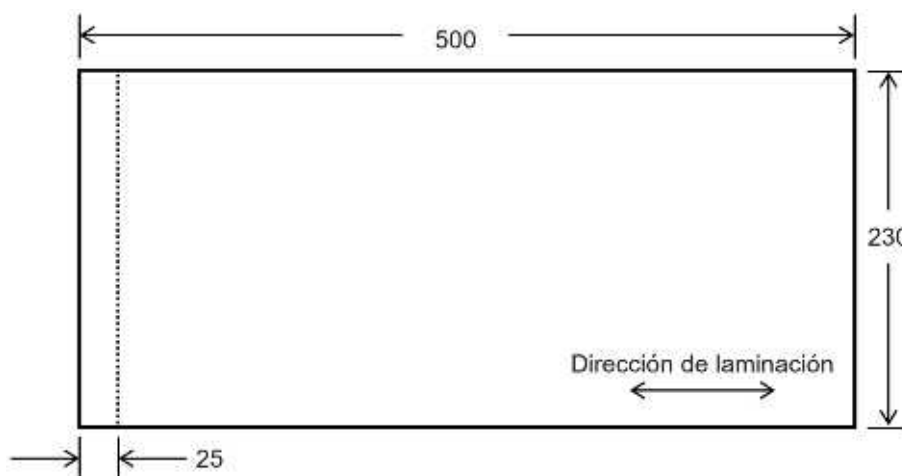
Dimensiones de las placas sometidas a ensayos de corte. La línea punteada marca el ancho de la probeta de corte. Dimensiones en milímetros.
